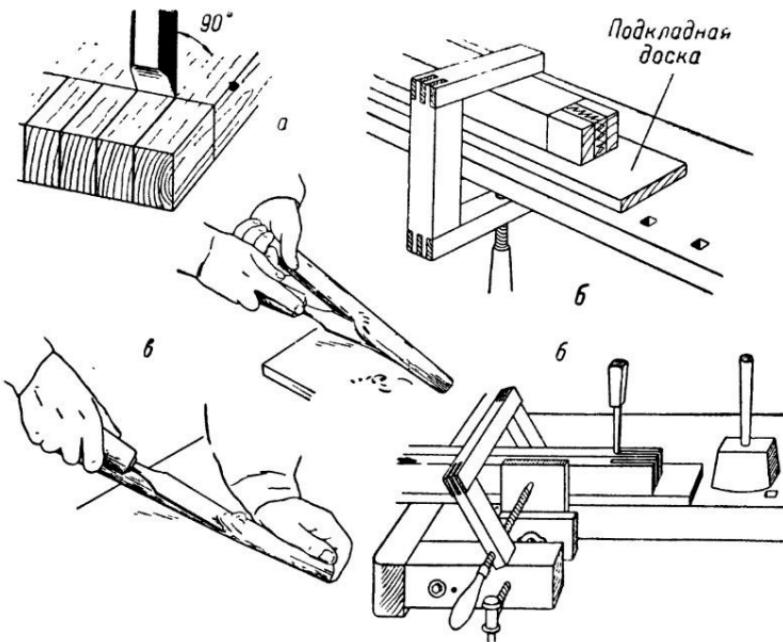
Приемы работы стамесками: а — положение стамески (долота) при долблении; б — закрепление деталей при долблении; в — нельзя держать руку перед инструментом.
